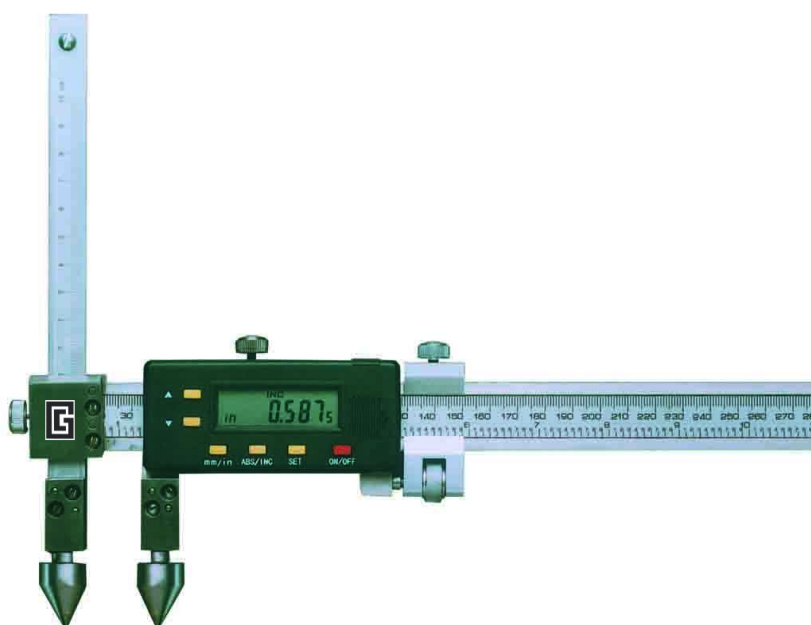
Общий вид штангенциркулей модели ШЦЦС-127
